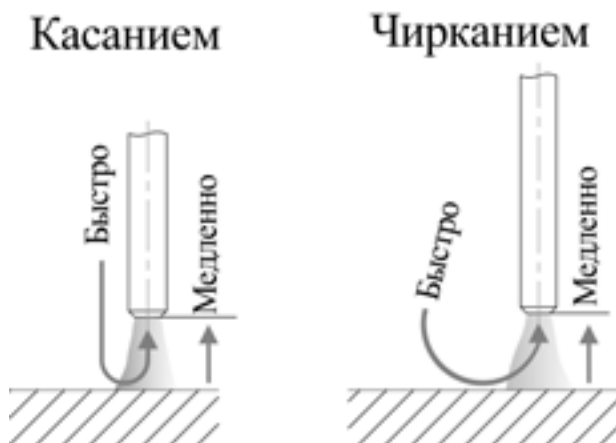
Способы зажигания сварочной дуги.
